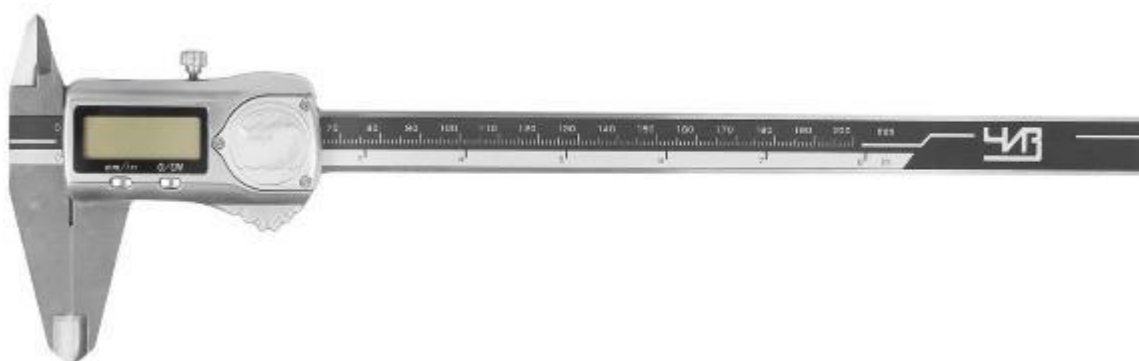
Общий вид штангенциркулей ШЦЦ-I
